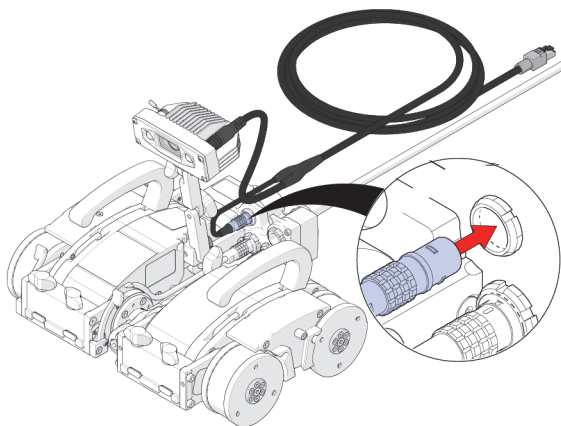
Collegamento del connettore di alimentazione della fotocamera all'ombelicale
